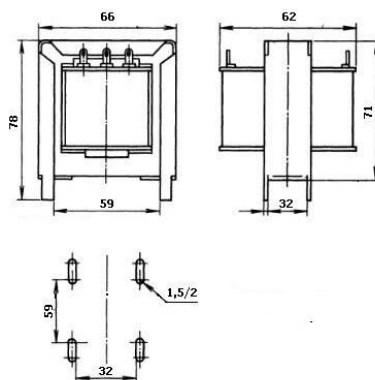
Габаритні розміри трансформатора В78386-Р1116-А "
